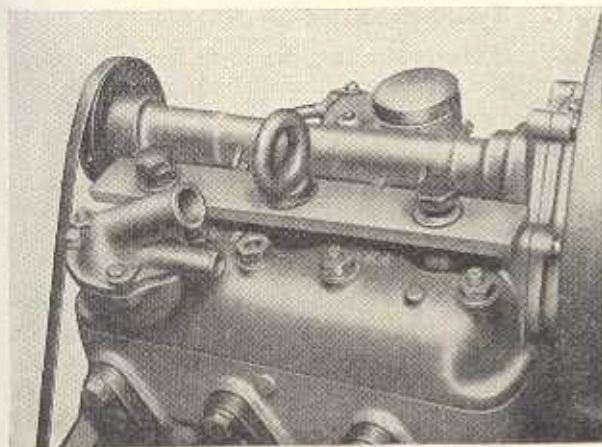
Aushebevorrichtung am Motorblock angeschraubt
